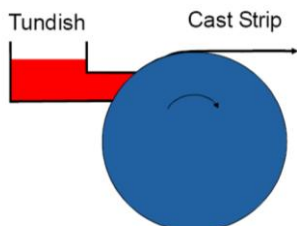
Representación esquemática de la máquina de colada de un solo tambor en dirección horizontal.
